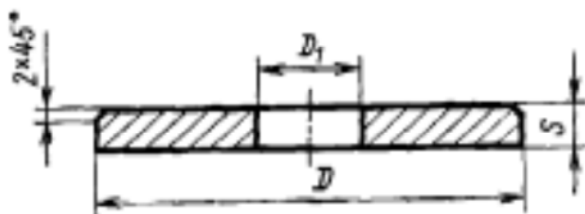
Конструкция и размеры опорной шайбы приспособления для удаления стержней
